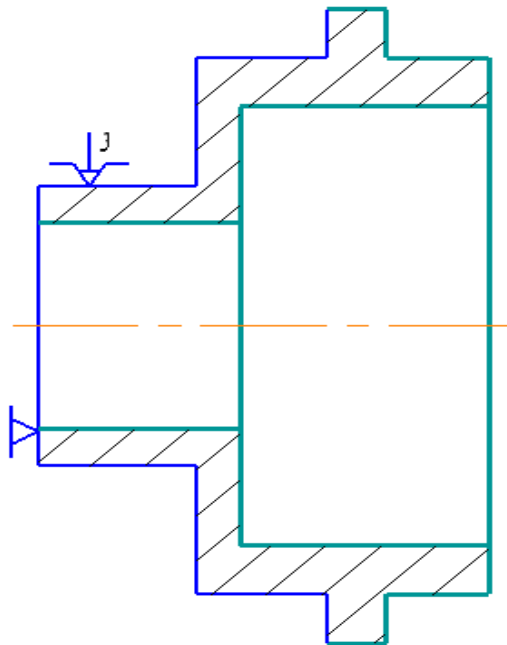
Схема базирования заготовки на токарной операции с ЧПУ
